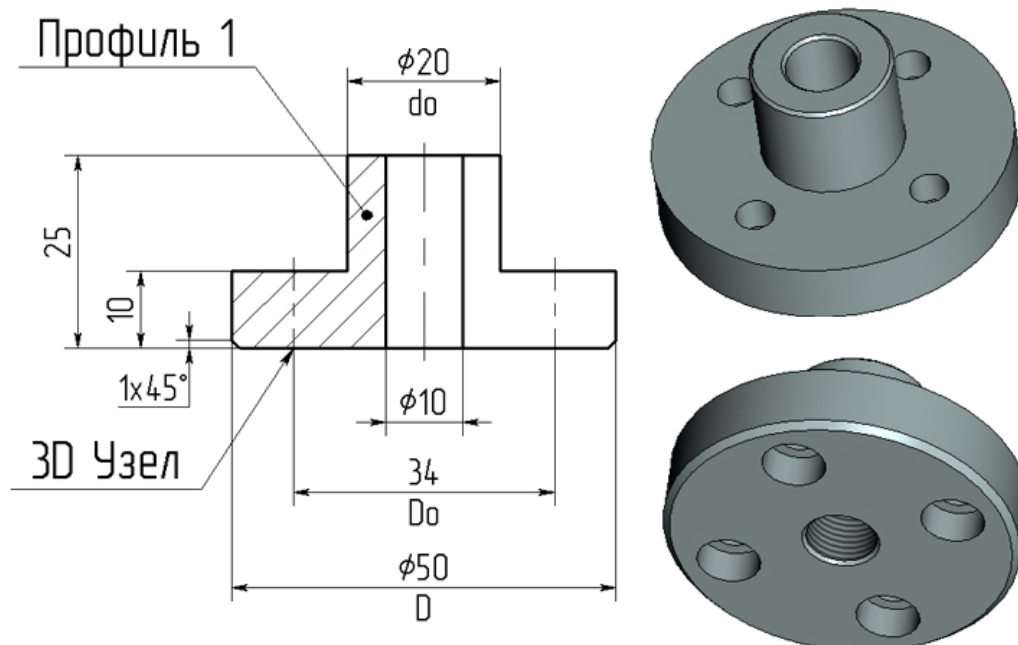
Чертеж и 3D модель детали «Крышка»
